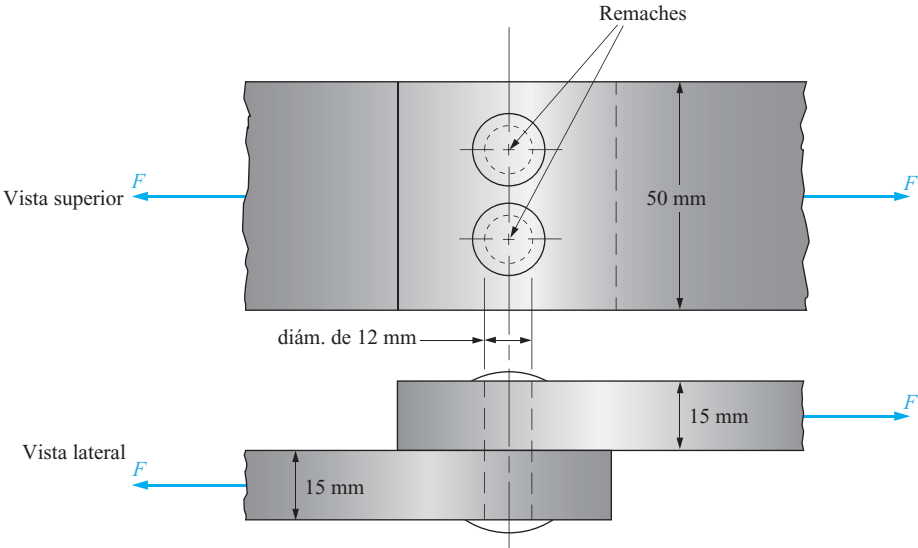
Junta traslapada remachada para el problema 1-70.
